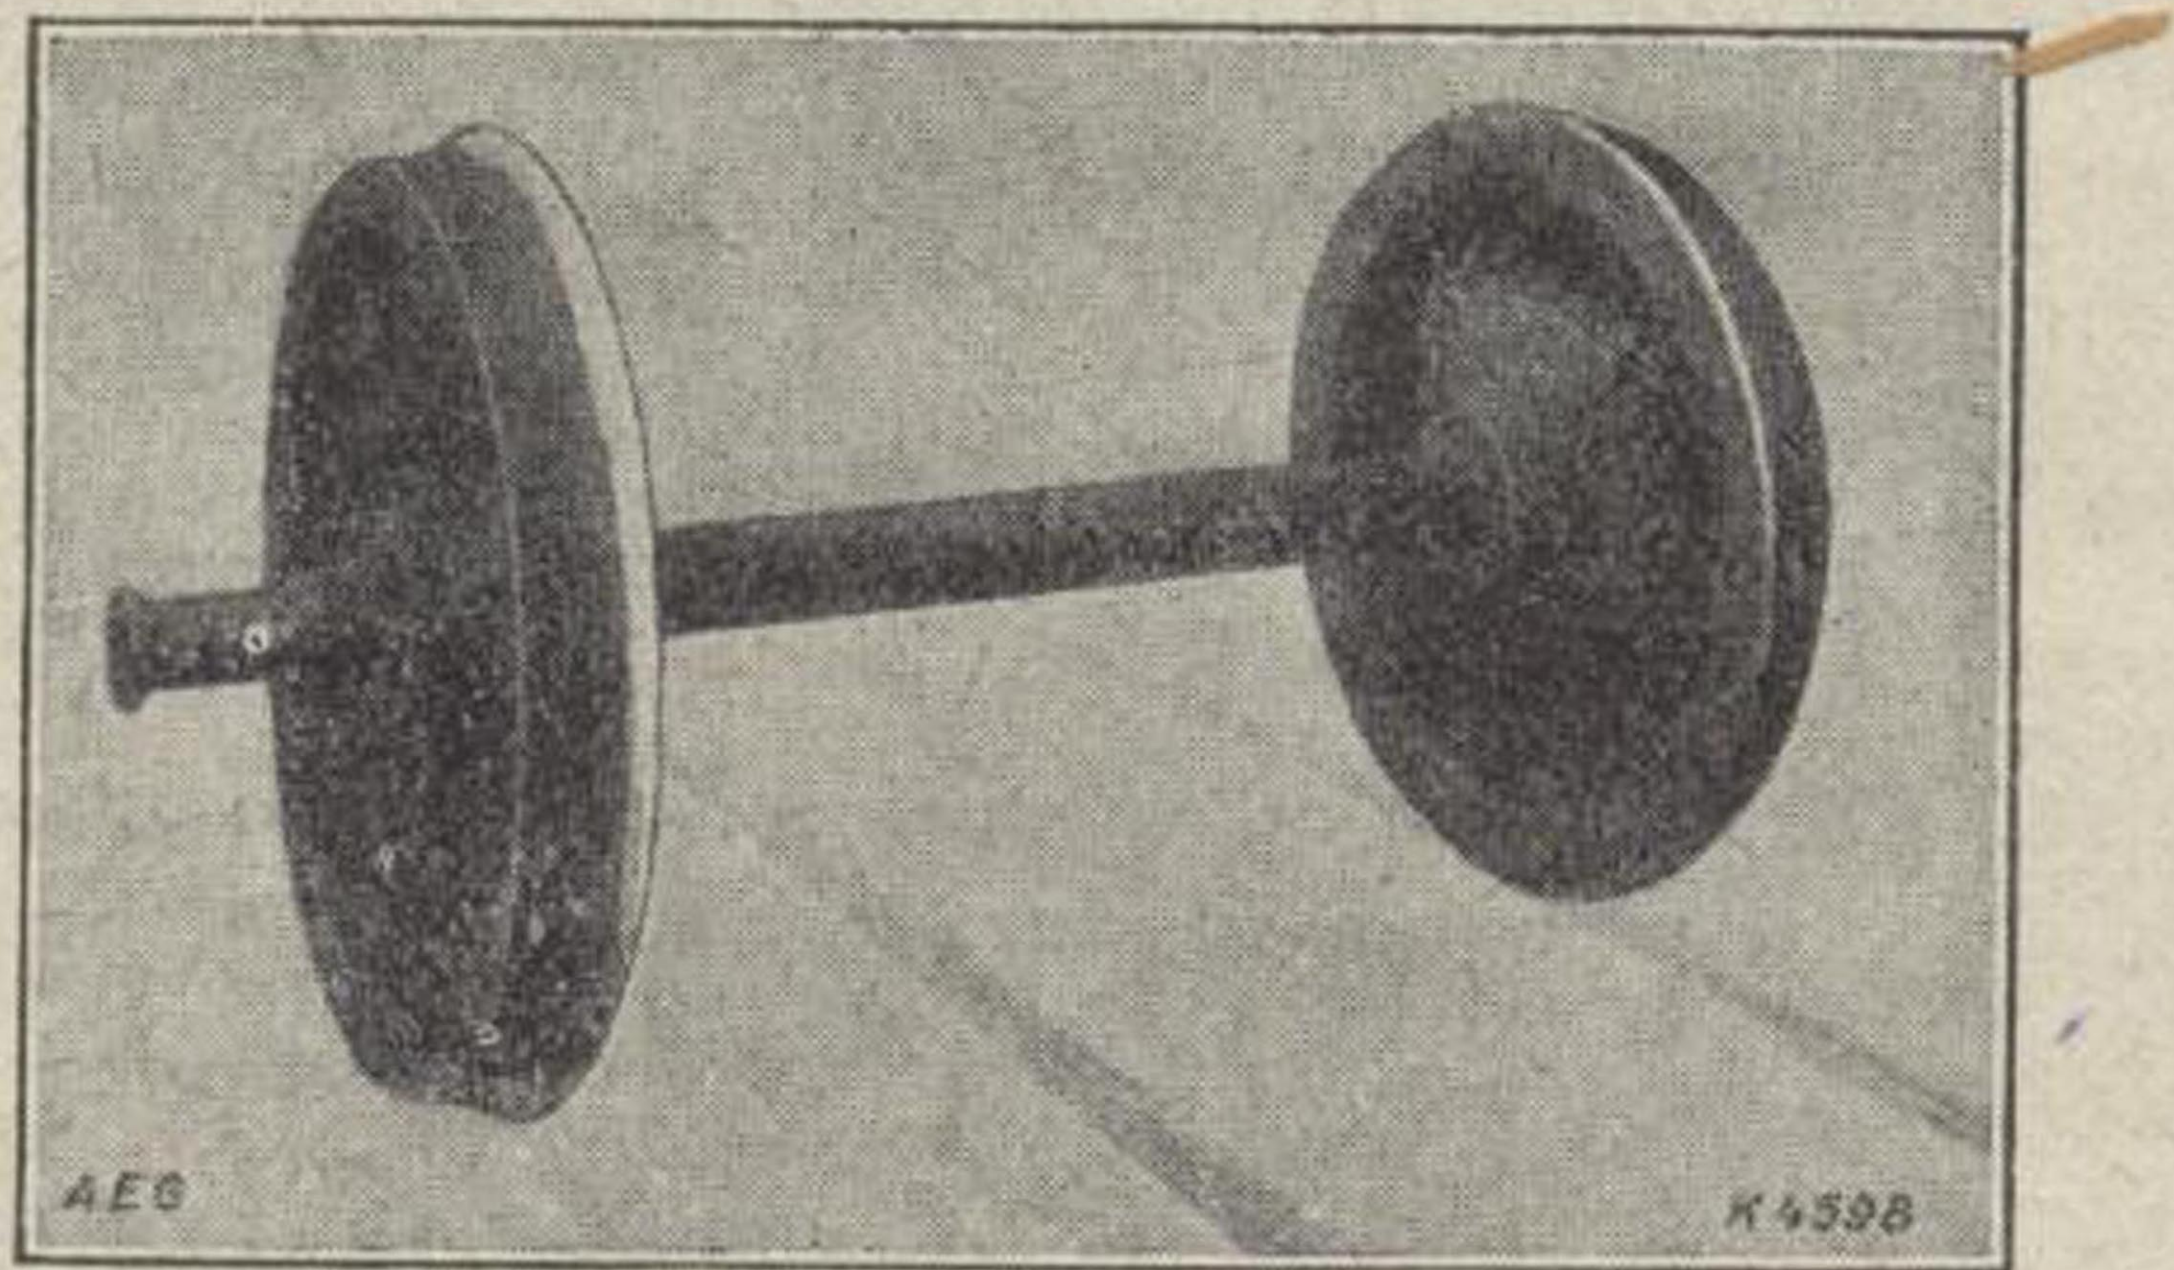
Llanta de rueda de ferrocarril reforzada con soldadura por arco.
